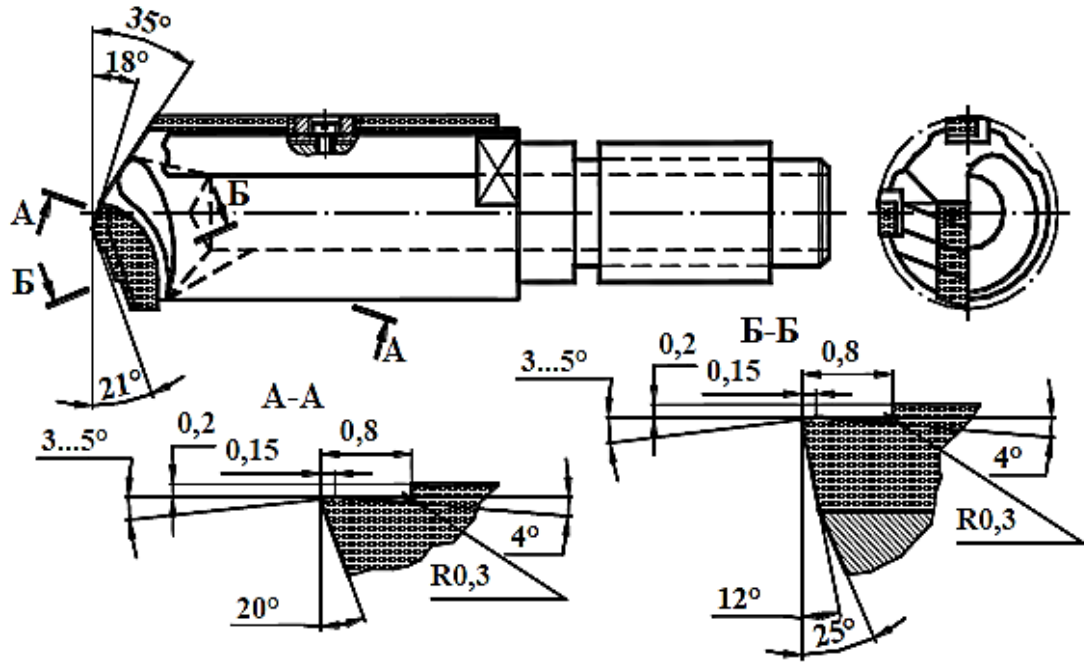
Одно різцеве свердло з напаяною ріжучою пластиною з твердого сплаву.
